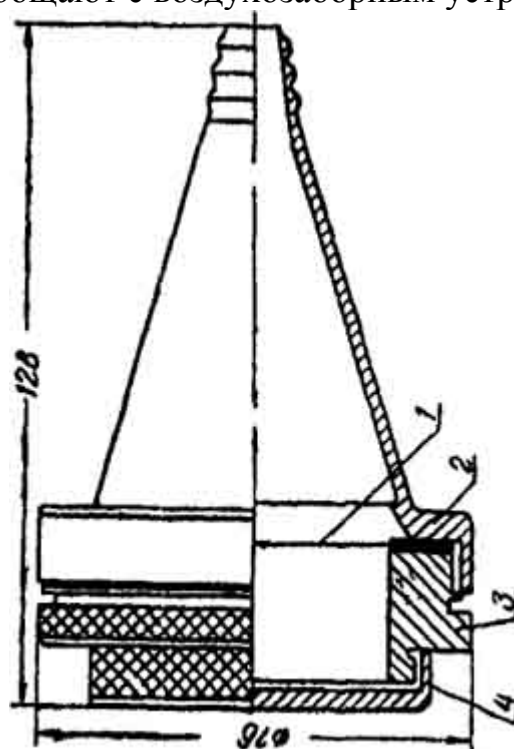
Металлический патрон для пылеулавливающего фильтра: 1 - фильтр, 2 - корпус, 3 - гайка, 4 - крышка.
